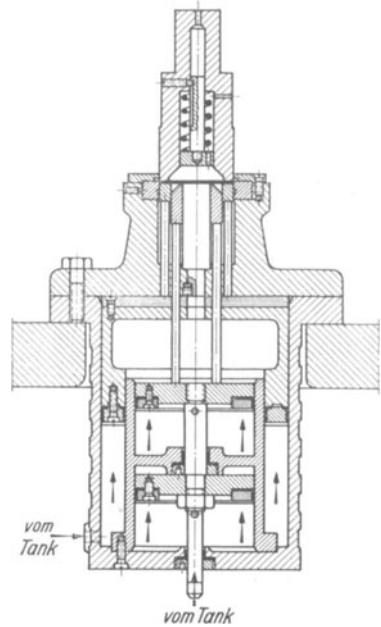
Verbundwerkzeug für Schneiden, Ziehen, Weiterziehen mit Preßluftniederhalter. Zur Erzeugung des notwendigen Preßluftdrucks bei dem beschränkten Raum sind 2 Preßluftzylinder hintereinander geschaltet (WEINGARTEN).
